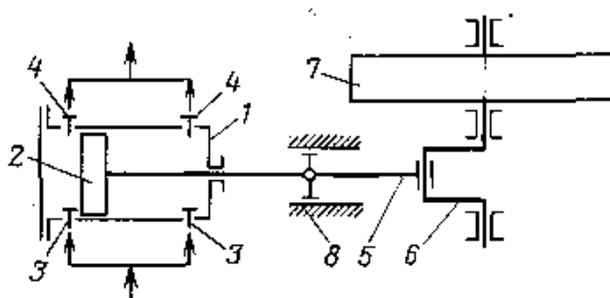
Одноцилиндровый компрессор двойного действия: 1 – цилиндр, 2 – поршень, 3 – всасывающий клапан, 4 – нагнетательный клапан, 5 – шатун, 6 – кривошип, 7 – маховик, 8 – крейцкопф
